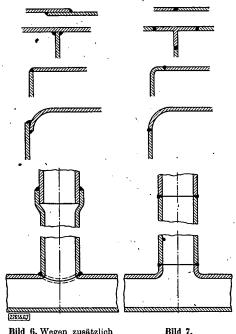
Wegen zusätzlich auftretender Beanspruchungen weniger brauchbare Ausführungen.
